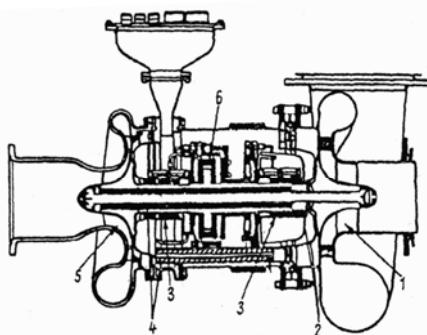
Турбокомпрессор на газовых подшипниках, работающий по циклу Брайтона: 1 - турбина; 2 - отражательный тепловой экран; 3 - подшипник; 4 - медные втулки; 5 - компрессор; 6 - упорный подшипник с самоустанавливающимися подушками
